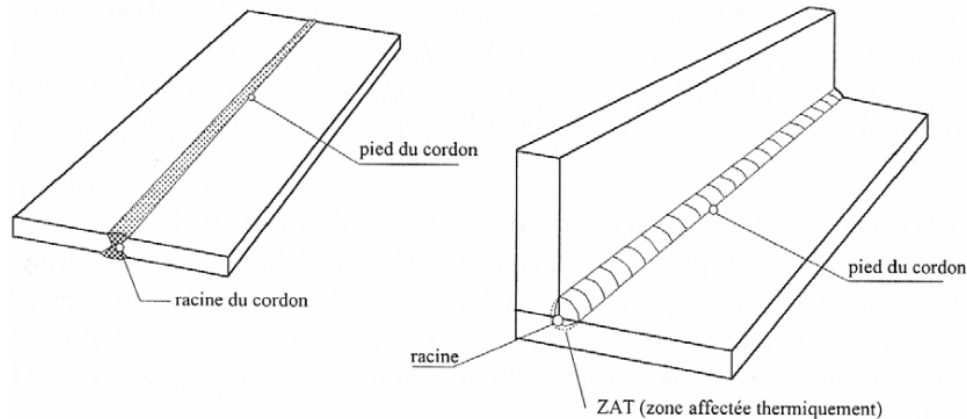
Liaison de deux pièces par soudage
